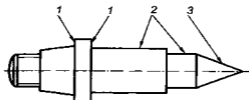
Виды поверхностей детали: 1 – плоские; 2 – цилиндрические; 3 – конические
